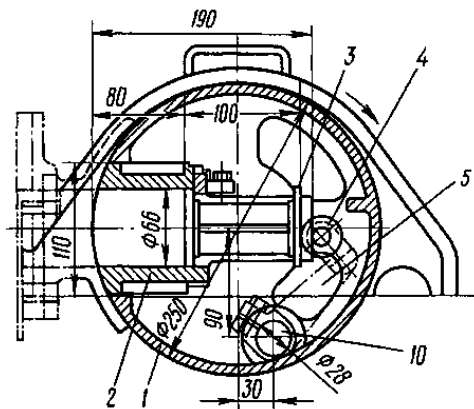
Подільна головка: 1 – чавунний барабан; 2 – циліндр; 3 – плавучий поршень; 4 – ролик; 5 – важель; 10 – обертальний валик
